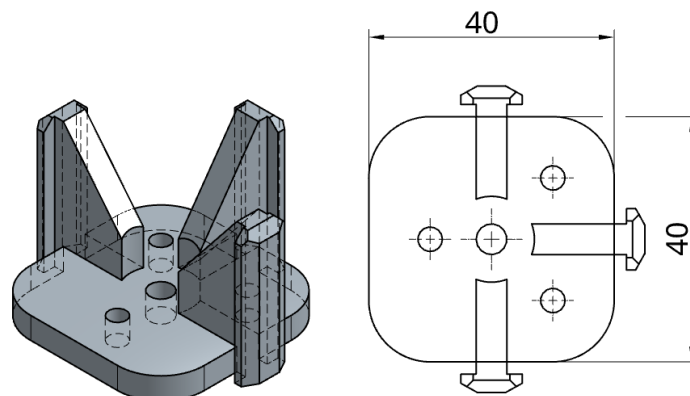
Montaje del eje Z al segundo brazo, vista isométrica y de planta, medidas en mm.
